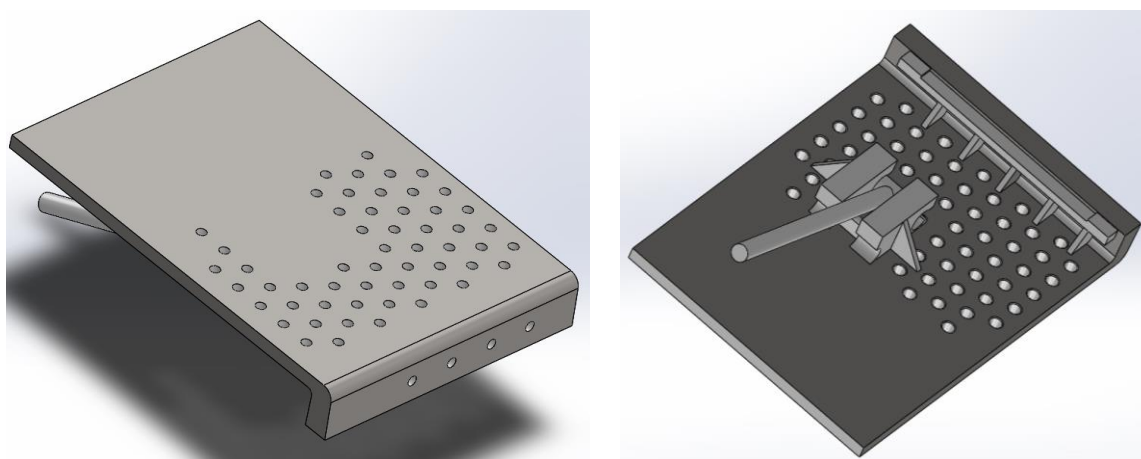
Montagem da Placa Proposta com o Pino de Fixação
